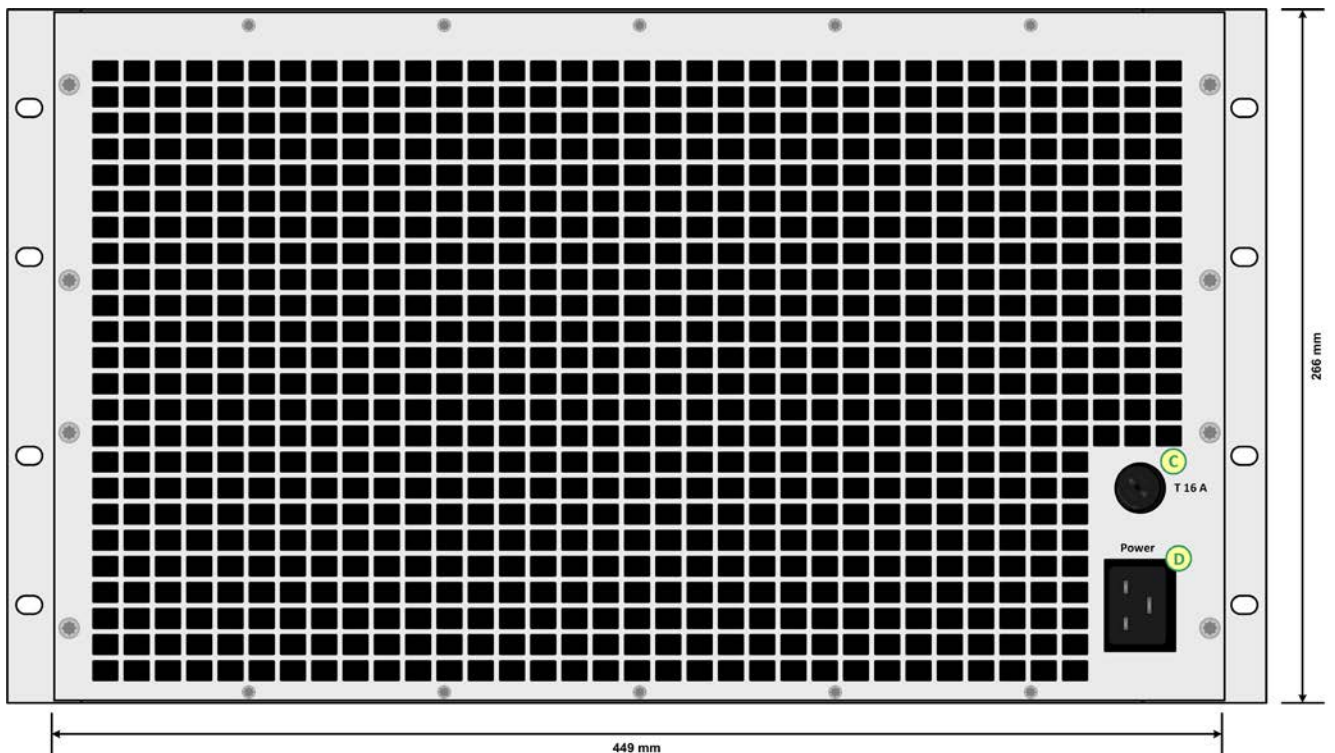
Vue arrière du châssis (rev. 01, obsolète)
